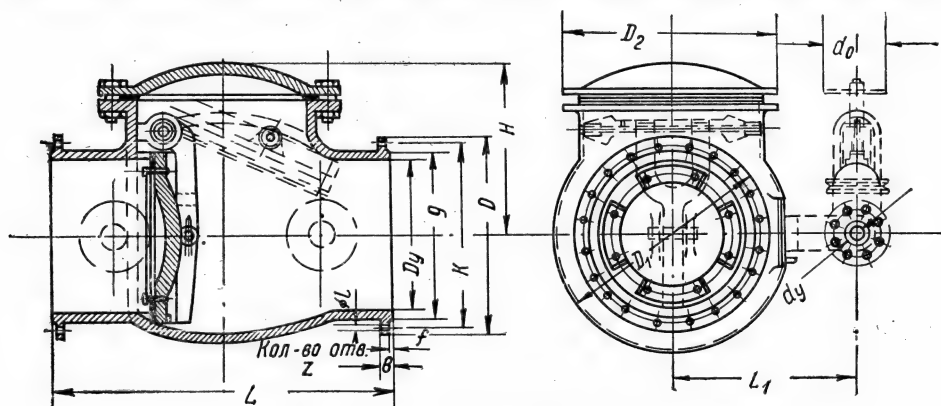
Клапан обратный поворотный 19ч16бр.
